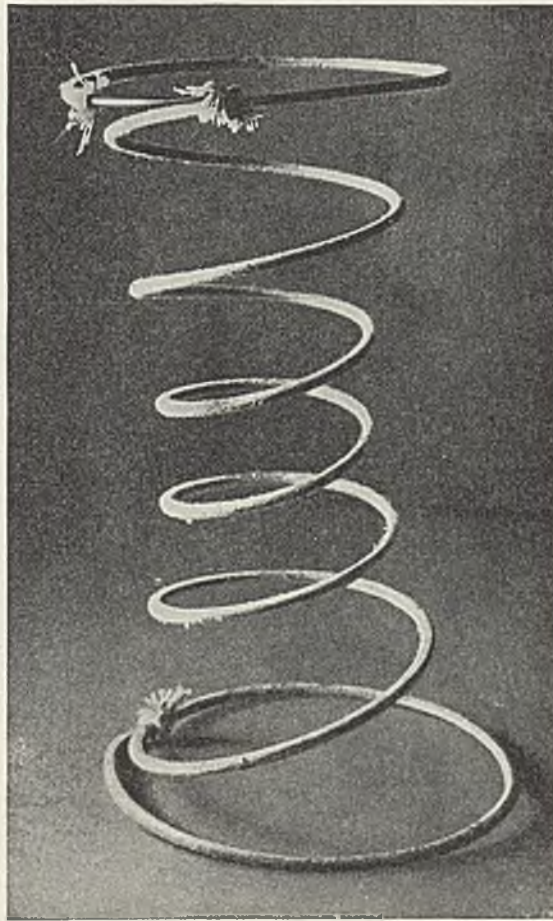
Die unspinnene Feder kann bei ihrem Stand auf Holz nicht klappern. Am oberen Ring ist ein Stück des Gewebes entfernt
